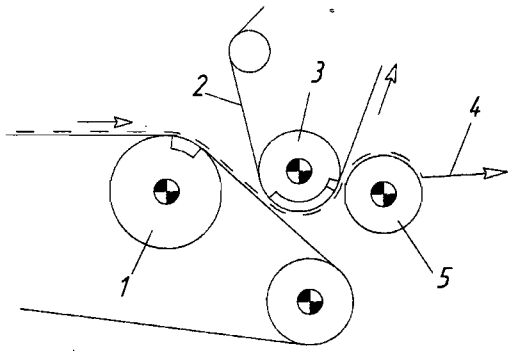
Универсальный пресс: 1 – гауч-вал; 2 – прессовое сукно; 3 – отсасывающий вал; 4 – бумажное полотно; 5 – гранитный вал
